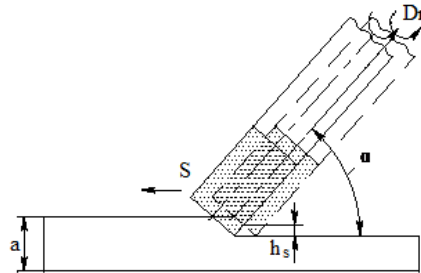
Пропонована схема обробки для встановлення залежностей сили різання від кута нахилу інструмента та подачі
